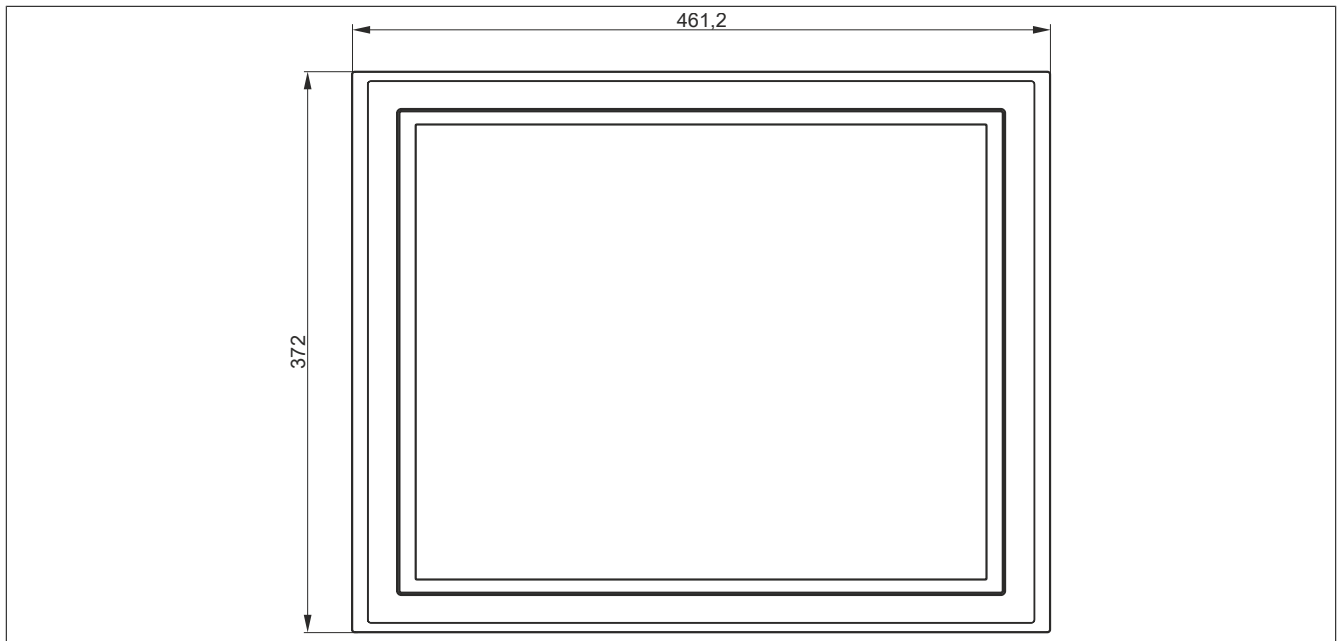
5AP5120.1906-000 - Abmessungen
